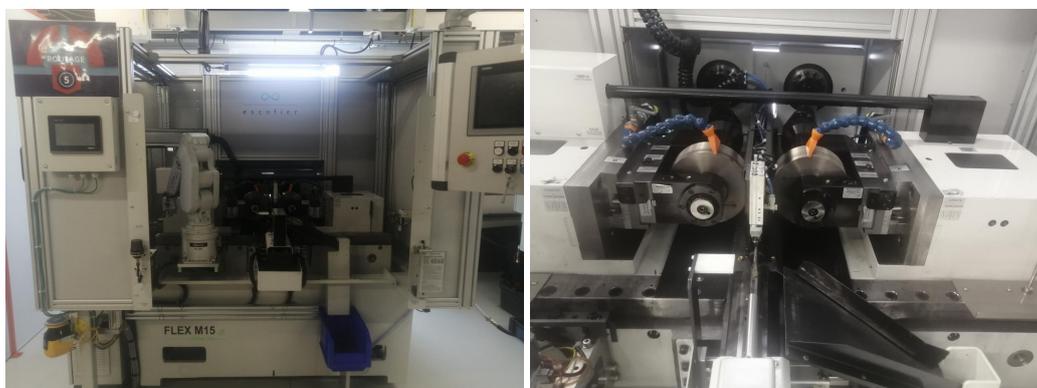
Pièce reprise sur le centre d'usinage horizontal
